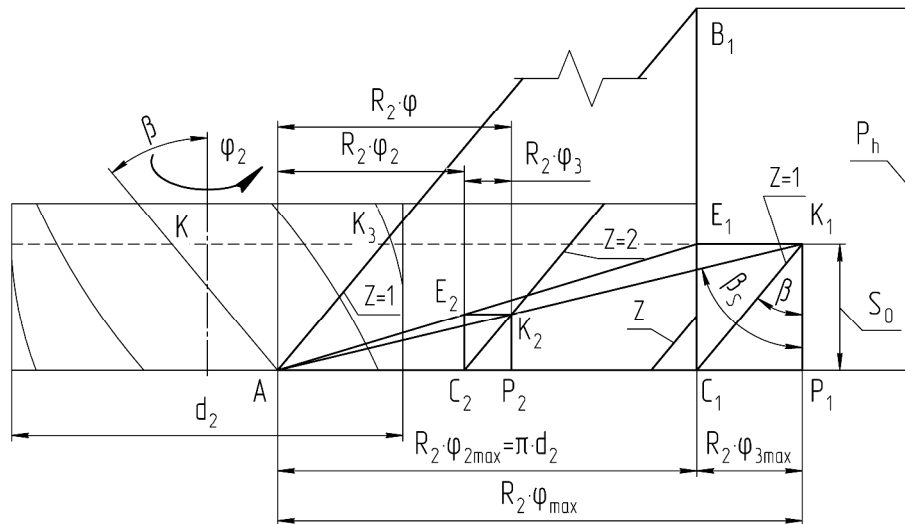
Параметри осьового руху дискової фрези при нарізанні гвинтових зубців циліндричного косозубого колеса
